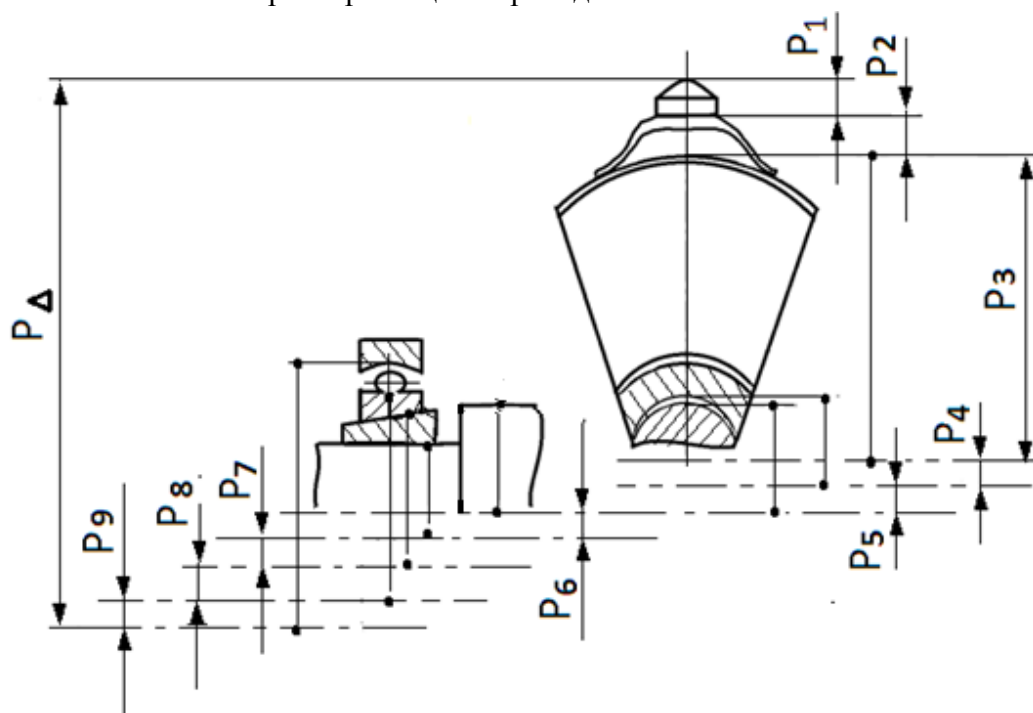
Размерная цепь формирования радиуса расположения вершин рабочего профиля бичей
